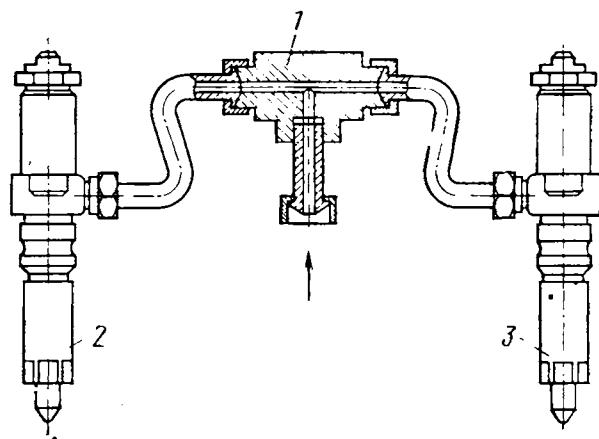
Крепление проверяемой и эталонной форсунки с помощью тройника
